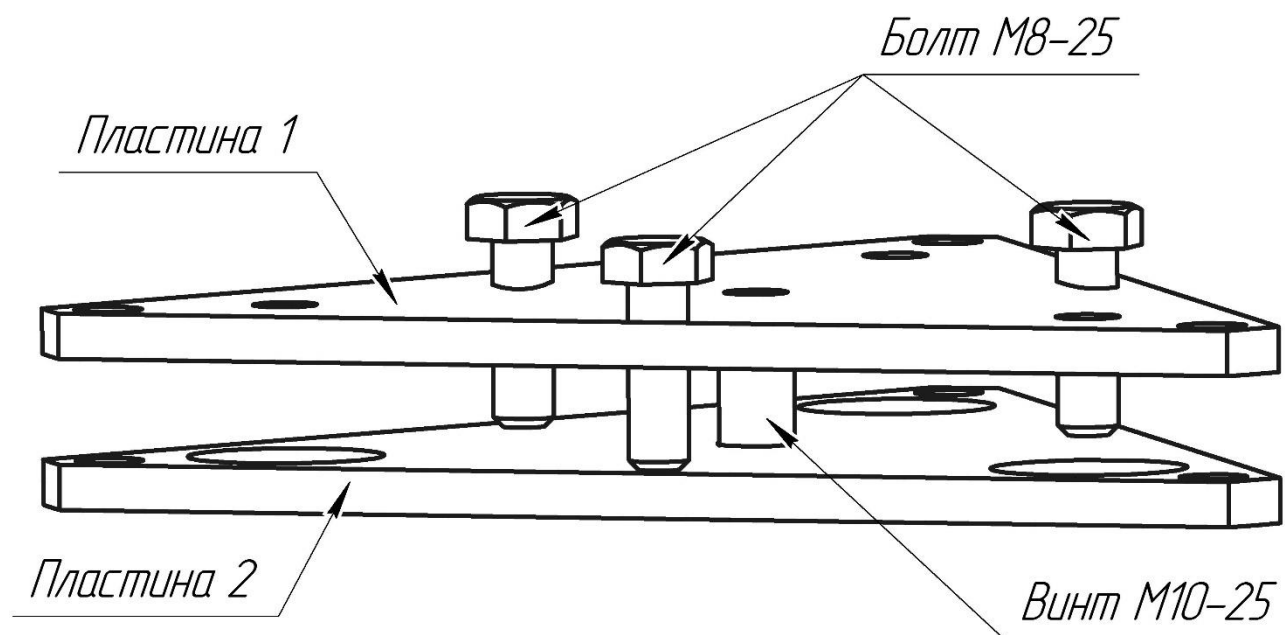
Крепление виброметра с регулировкой – Шаг 1
